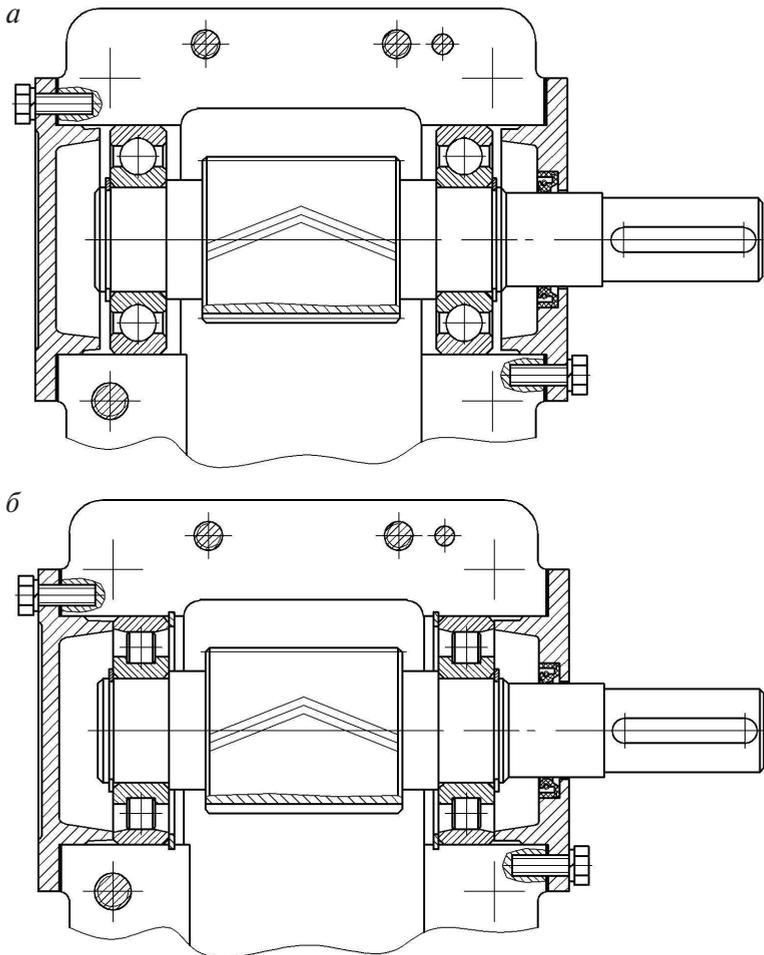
Варианты конструктивного исполнения плавающего вала:
